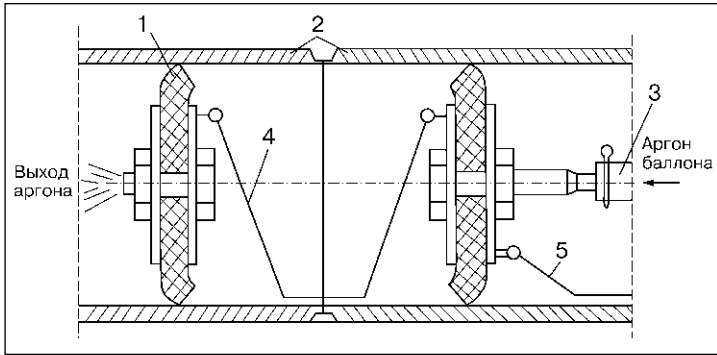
Приспособление для защиты обратной стороны шва аргоном: 1 — заглушка из резины; 2 — свариваемые трубы; 3 — резиновый рукав; 4, 5 — тросики
